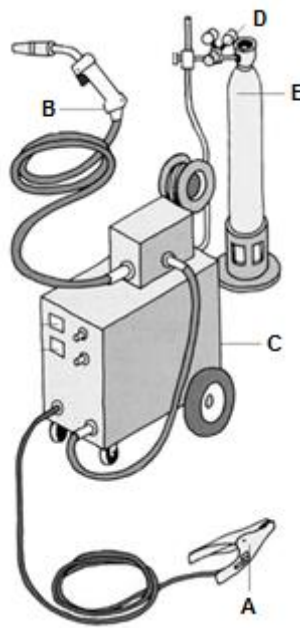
Sistema de soldadura MAG (23).
